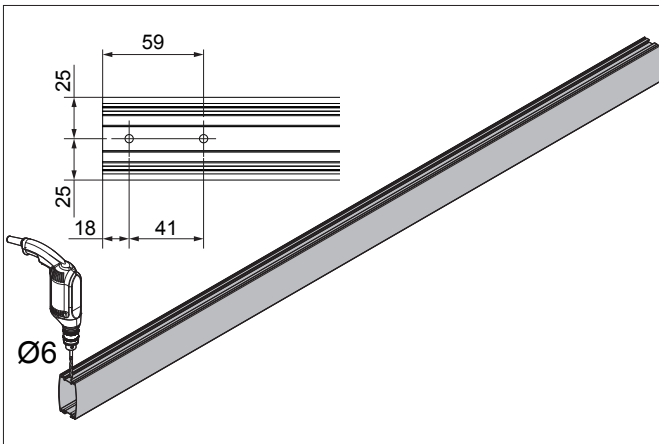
INSTALLAZIONE ASTA FISSA / FIX BAR INSTALLATION
